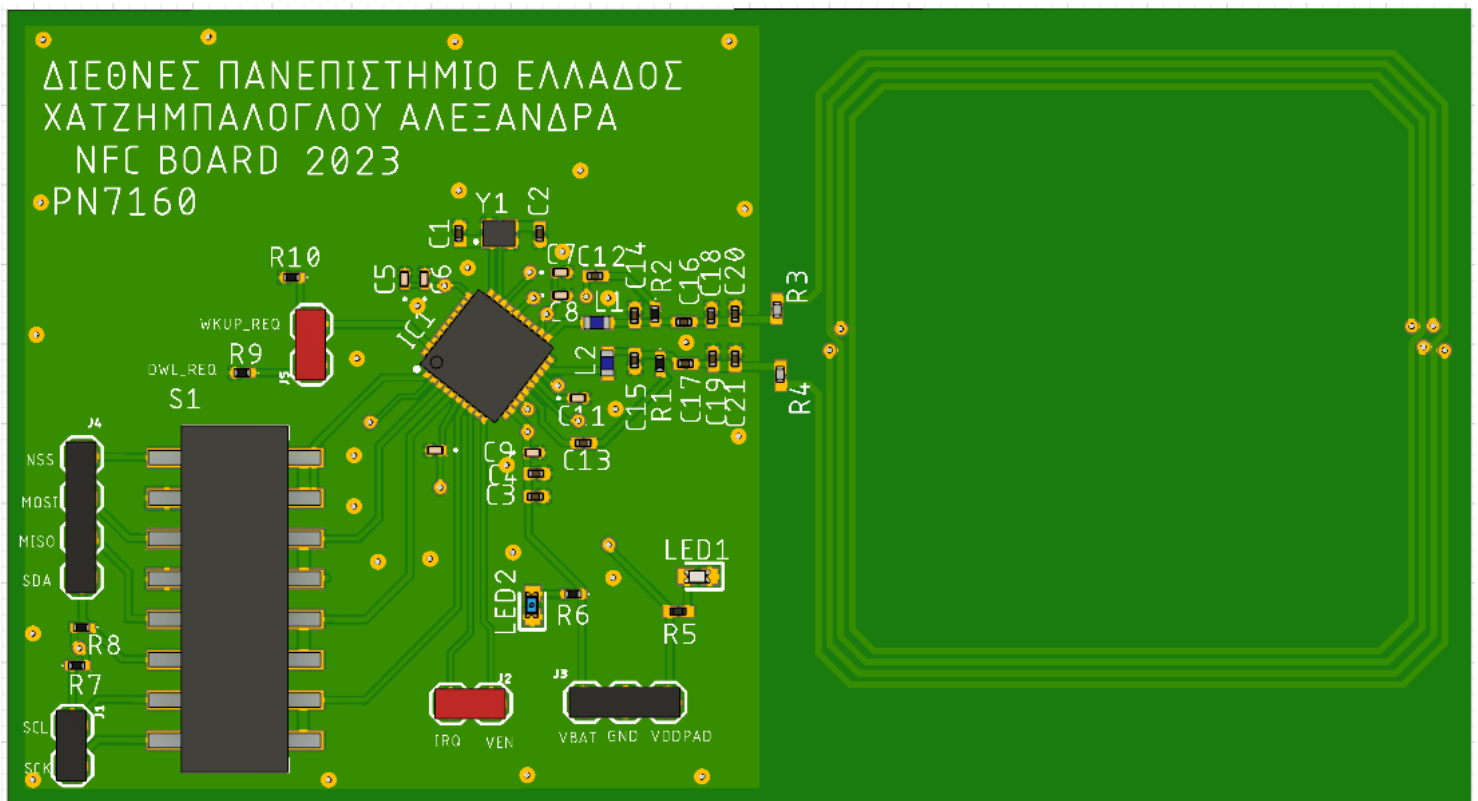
Board στο Eagle Bottom view χωρίς Ratsnet.
